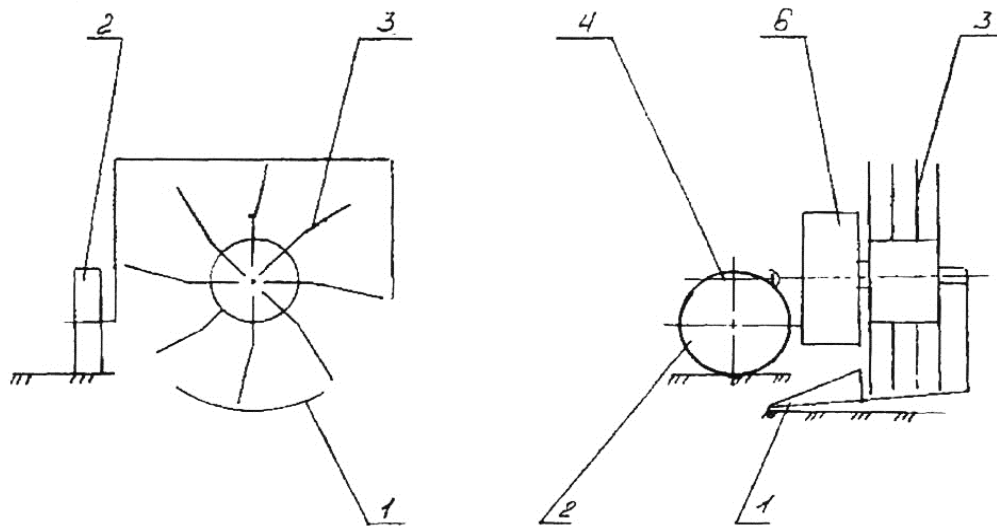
Конструктивна схема копача роторного типу: 1 – леміш; 2 – пристрій для регулювання глибини підкопування (опорне колесо); 3 – ротор пальчастий; 4 – механізм привода копача; 6 – редуктор
